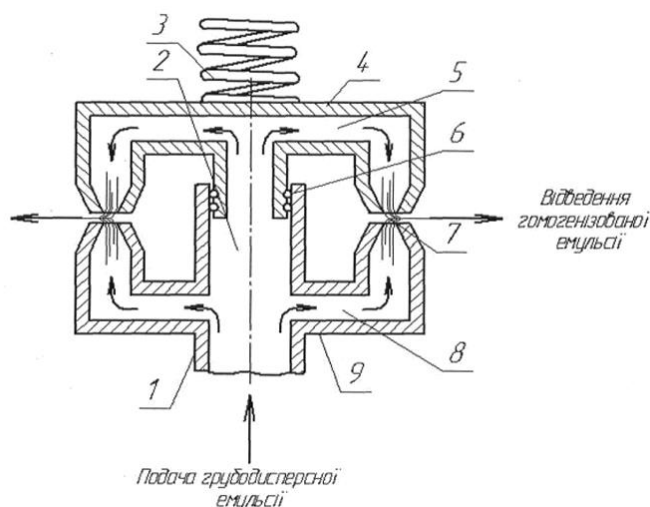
Конструктивна схема робочої головки клапанного гомогенізатора:
